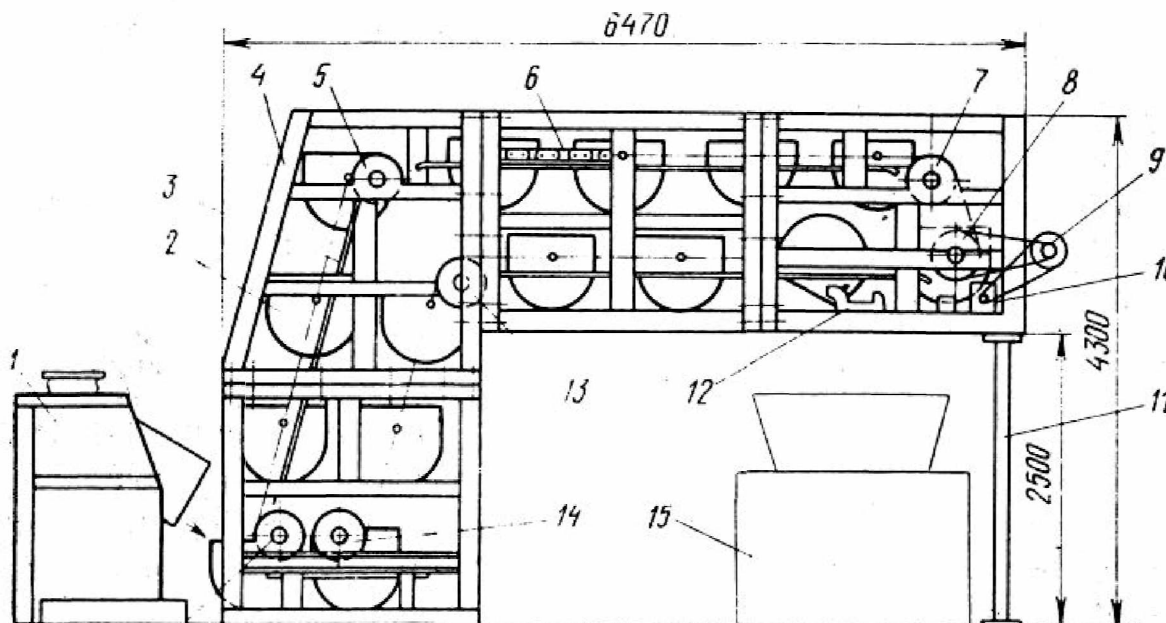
Ковшовий ланцюговий конвеєр Ш2-ХББ: тістомісильна машина; 2 – ємності; 3 – напрямні, 4 – каркас; 5, 7, 13, 16 – зірочки; 6 – втулково-роликові ланцюги; 8 – привідна пара зірочок; 9 – проміжний вал; 10 – черв'ячний редуктор; 11 – стійки; 12 – механізм для повороту ємності; 14 – натяжна пара зірочок; 15 – тістоподільник.
